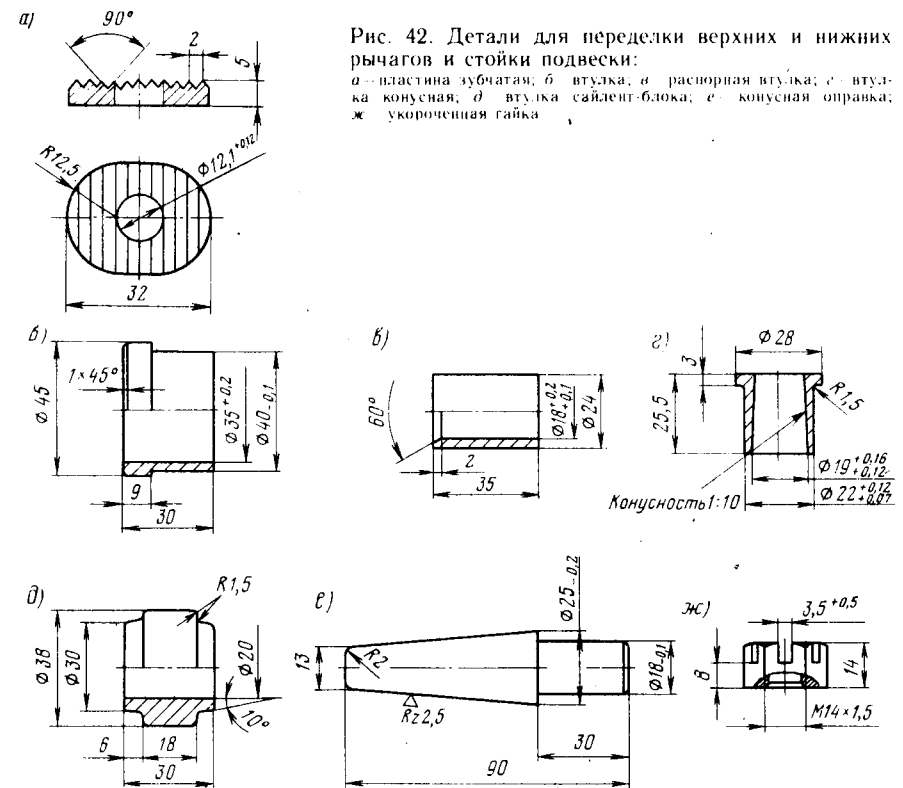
Детали для переделки верхних и нижних рычагов и стойки подвески:
